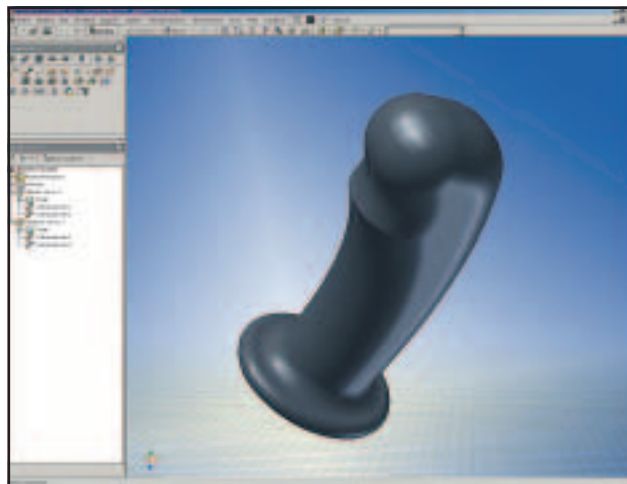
3D-модель сборки ручки джойстика в Autodesk Inventor
